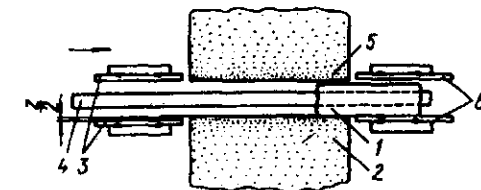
Схема установки направляющих линеек: 1 – обрабатываемая деталь; 2 – ведущий круг; 3 – направляющие линейки на входе; 4 – опорный нож; 5 – шлифовальный круг; 6 – направляющие линейки на выходе
